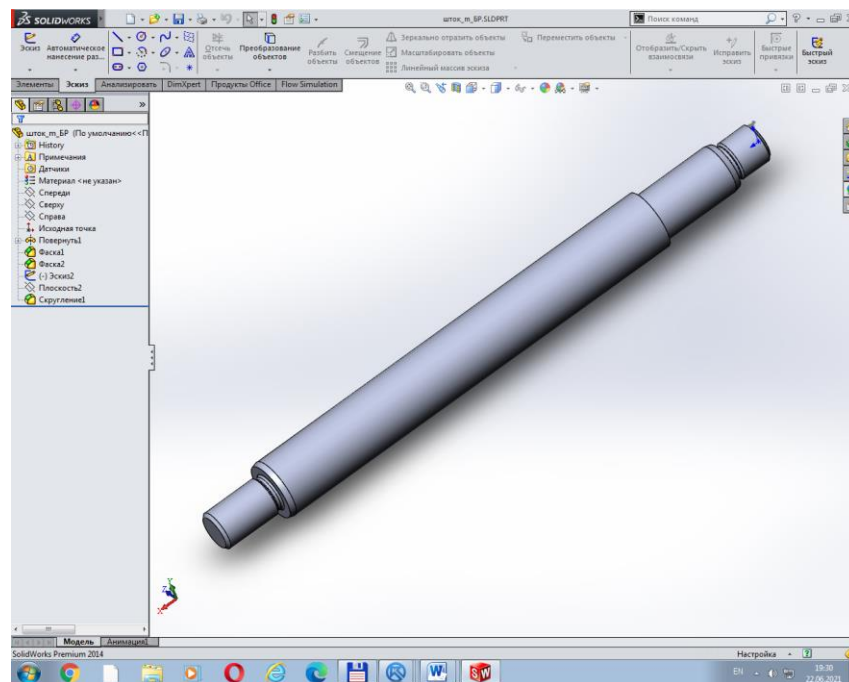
Модель деталі для обробки циліндричних поверхонь
